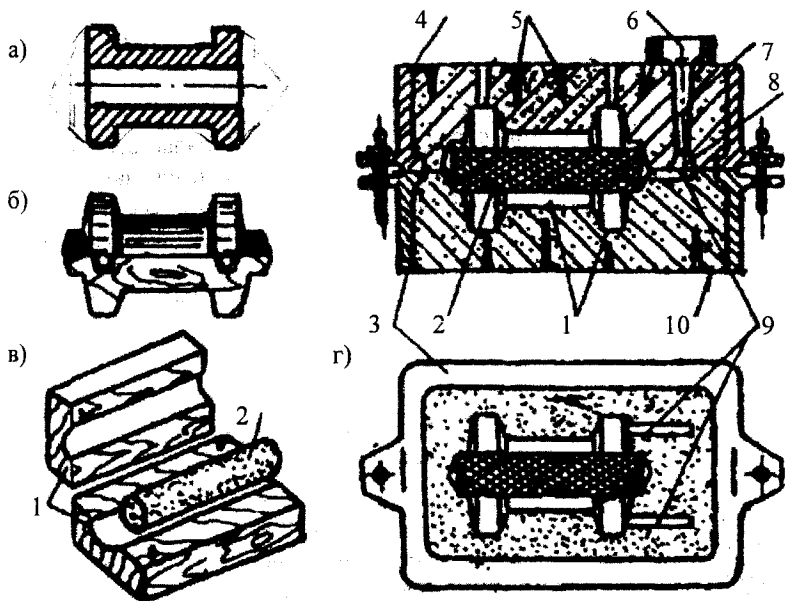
Процес виготовлення виливка литтям в піщані форми
